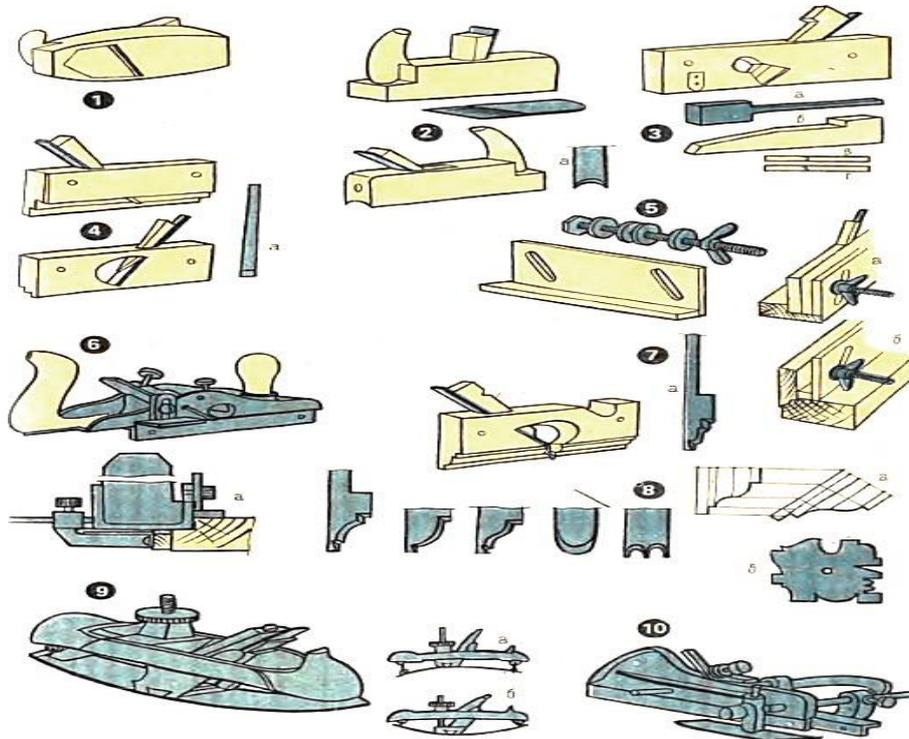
Рубанки специального назначения: 1 - штифтик с косым ножом; 2 - цинубель: а - нож цинубеля; 3 - зензубель: а - нож; б - клин; в - прямой зензубель (вид снизу): г - то же, косозубый; 4 - отборник (четверочник): а - нож; 5 - переставной универсальный упор: а, б - способы применения; 6 - универсальный отборник: а - схема действия (разрез); 7 - калевка: а - нож; 8 - ножи калевков: а - схема разворачивания профиля; б - калевочный шаблон; 9 - горбач универсальный: а - подъем для выпуклой детали; а, б - формы установки подошвы; 10 - шпунтубель малый металлический
